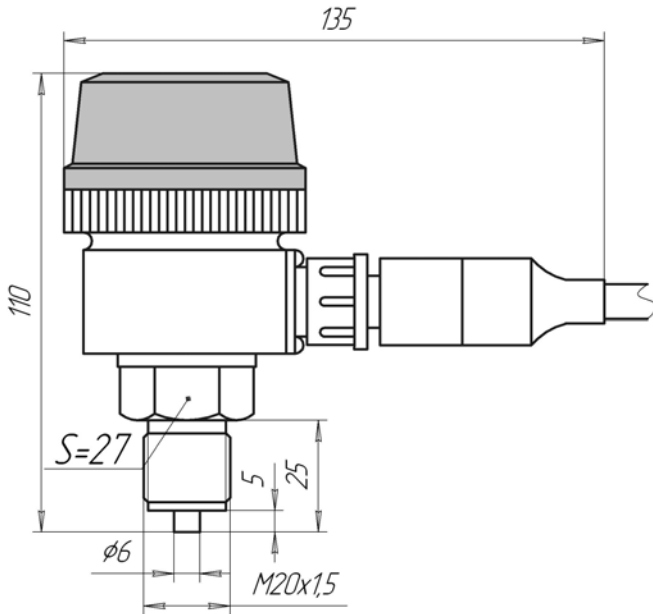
Модель 1020. Нержавеющий корпус, герморазъем.
